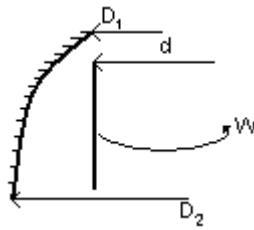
Конструкція з параболічною формою твірної кожуха та циліндричною формою твірної шнека
